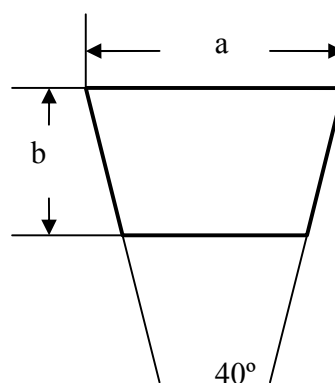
Características de la sección transversal de las bandas trapezoidales. (Fuente: Shigley 2001)
